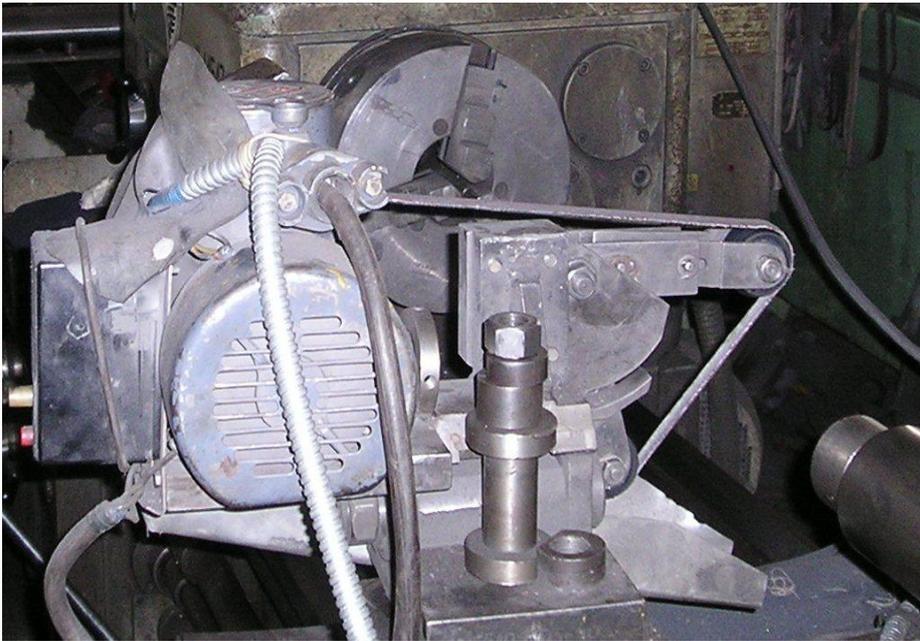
Устройство ленточного полирования на суппорте станка мод.1М63.
